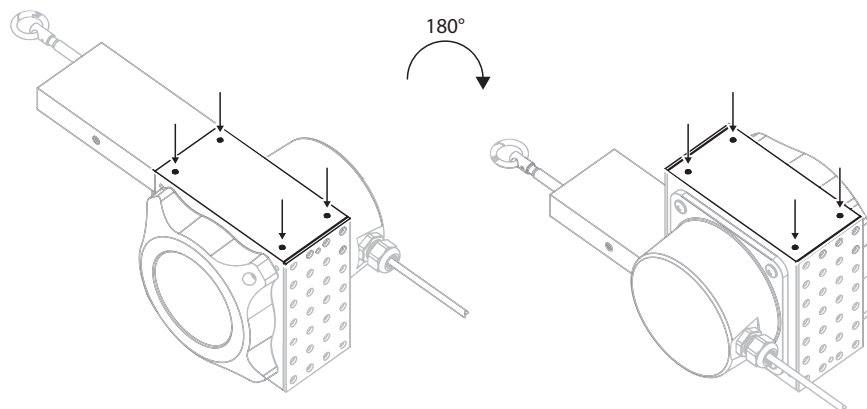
Befestigungsbohrungen DWE-...-120-...
